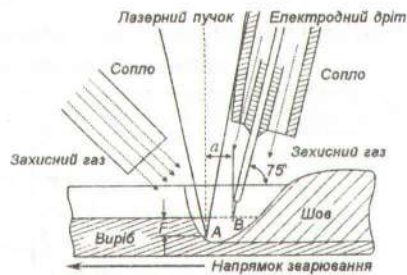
Лазерно-дугове зварювання при використанні електричної дуги з плавким електродом:
